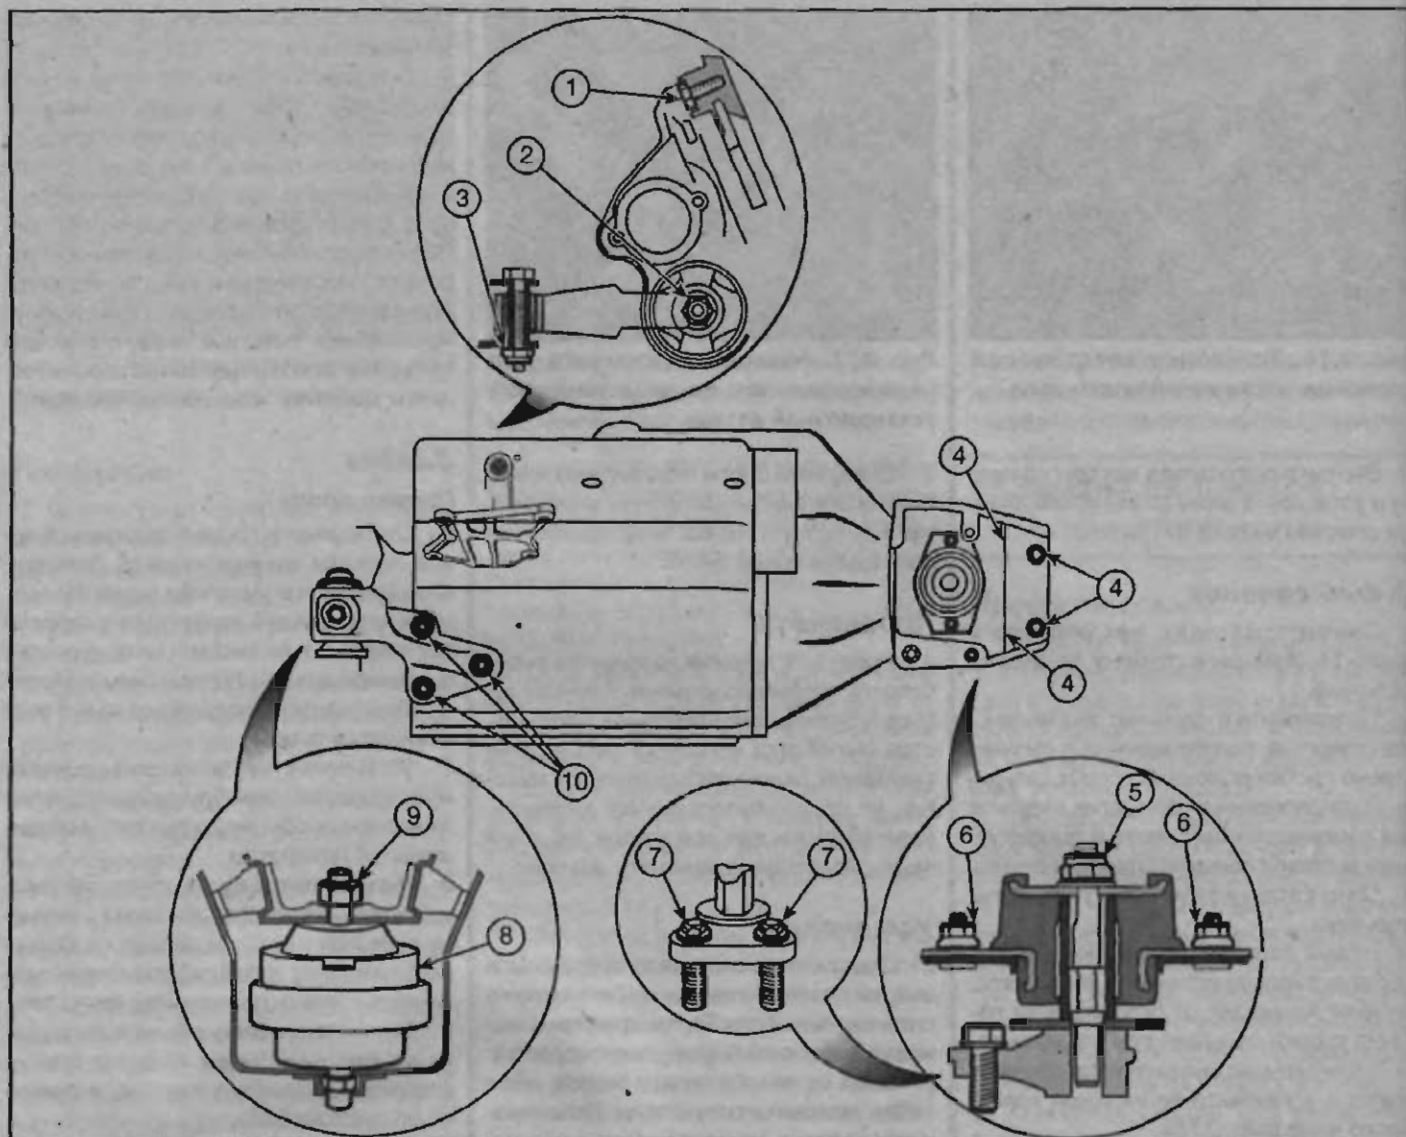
Опоры двигателя/коробки передач: 1 – болты крепления кронштейна задней опоры к блоку цилиндров; 2 – болт крепления задней опоры, соединяющий тягу с кронштейном блока цилиндров; 3 – болт крепления задней опоры, соединяющий тягу с нижней рамой; 4 – болт крепления кронштейна левой опоры к кузову; 5 – центральная гайка крепления резиновой подушки левой опоры; 6 – гайки крепления левой резиновой подушки к кронштейну; 7 – болты крепления левой резиновой подушки к коробке передач; 8 – правая резиновая подушка; 9 – центральная гайка крепления резиновой подушки; 10 – верхние болты крепления кронштейна опоры к двигателю
